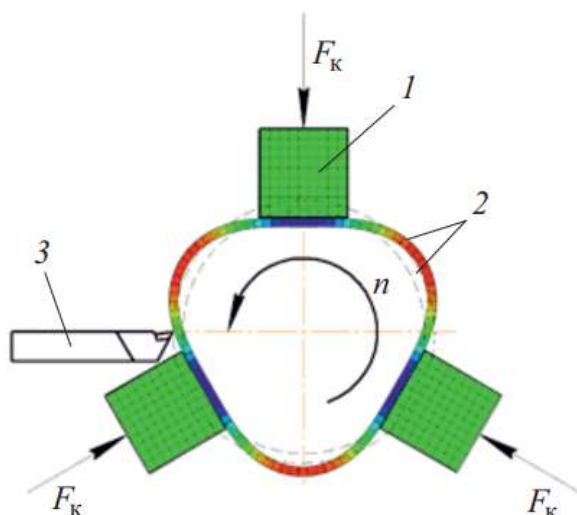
Деформація деталі при токарній обробці в трьох кулачковому патроні
